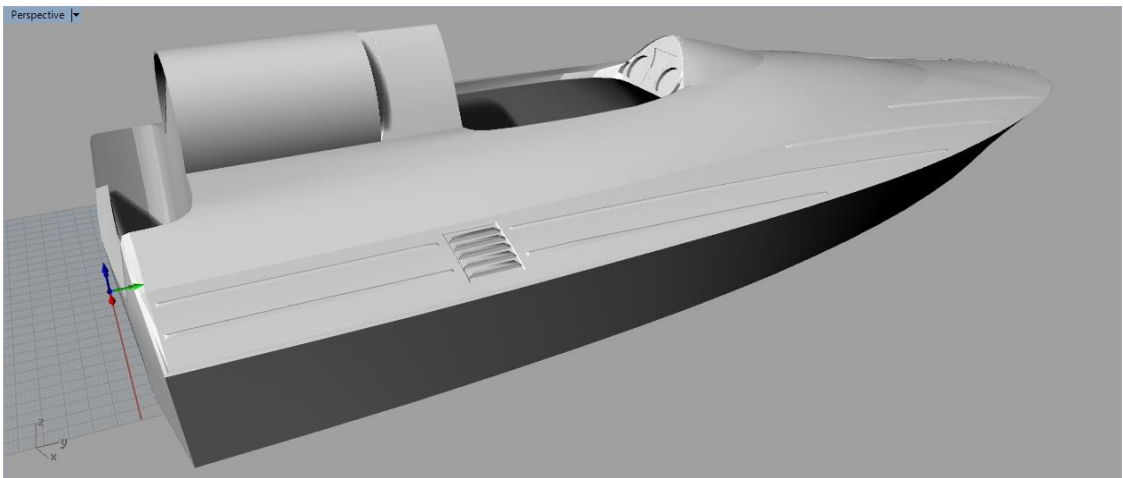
3D-модель корпуса гоночной лодки (race boat)
